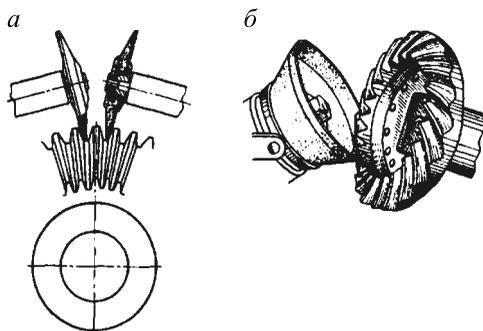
Схемы зубошлифования конического зубчатого колеса:
